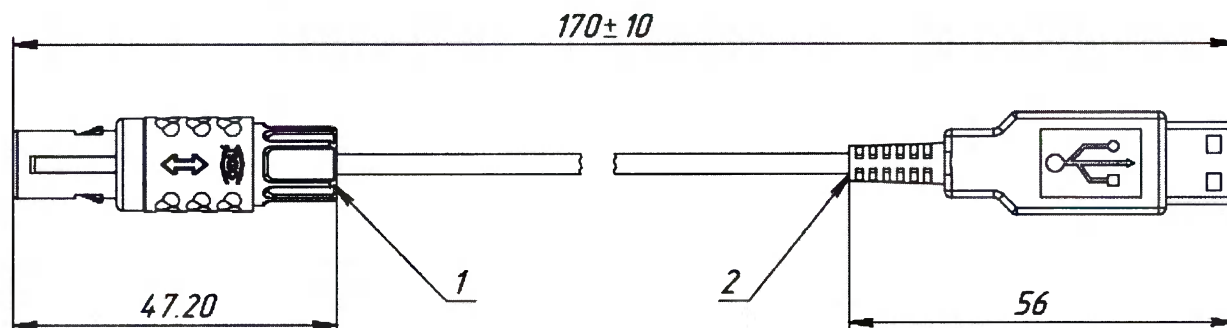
Внешний вид и габаритные размеры кабеля питания
